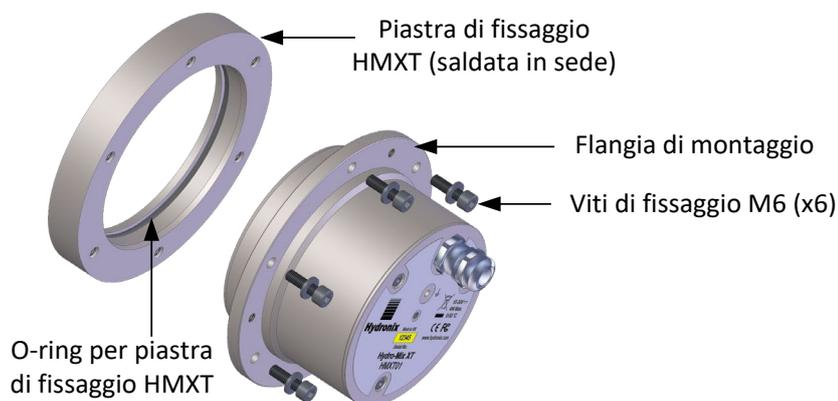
Componenti di montaggio del sensore Hydro-Mix XT
